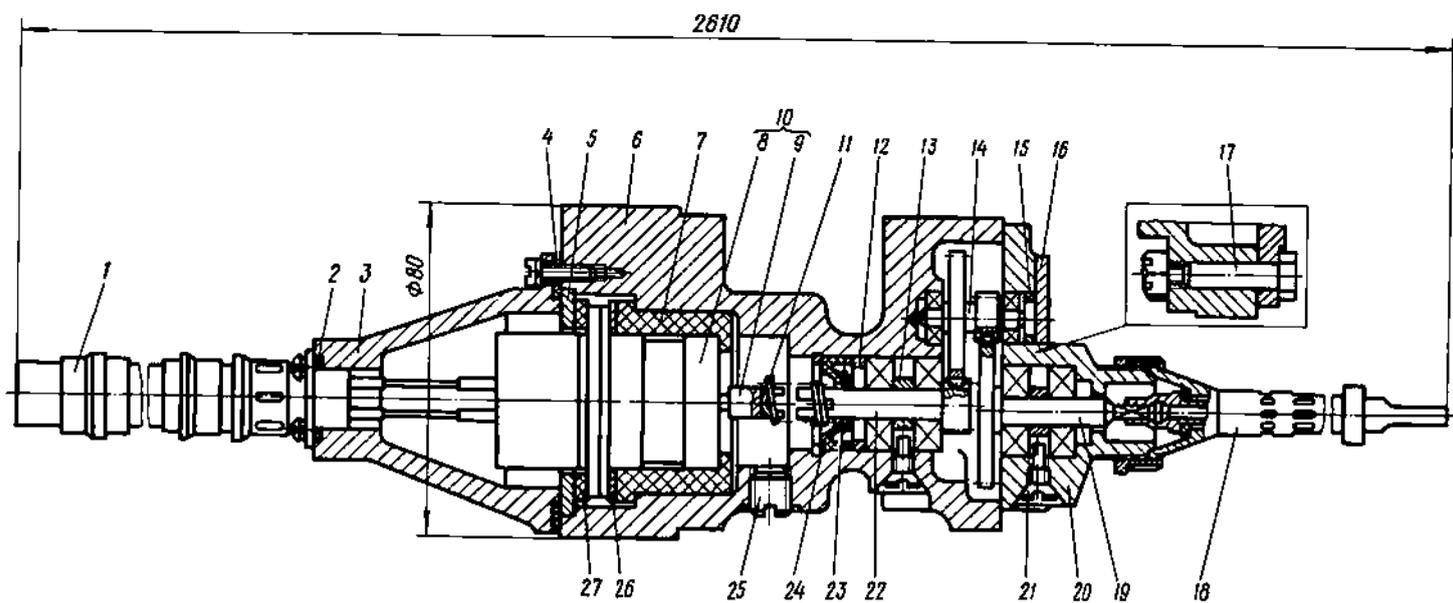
РЕДУКТОР С ТАХОГЕНЕРАТОРОМ 172.44.004с6
